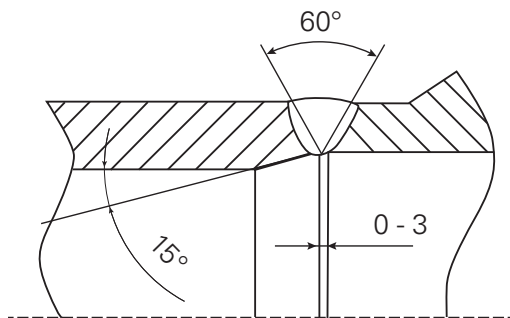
Rohr/Rohr Verbindung
